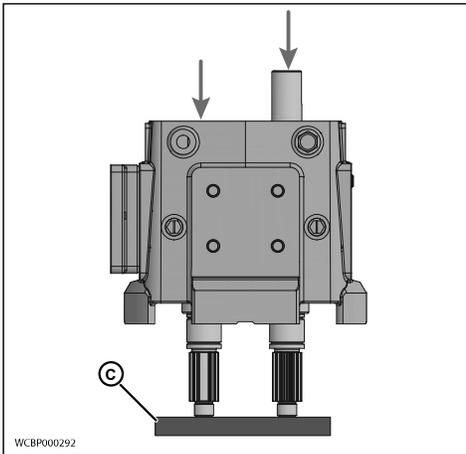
Presionar los ejes desde la caja de engranajes
